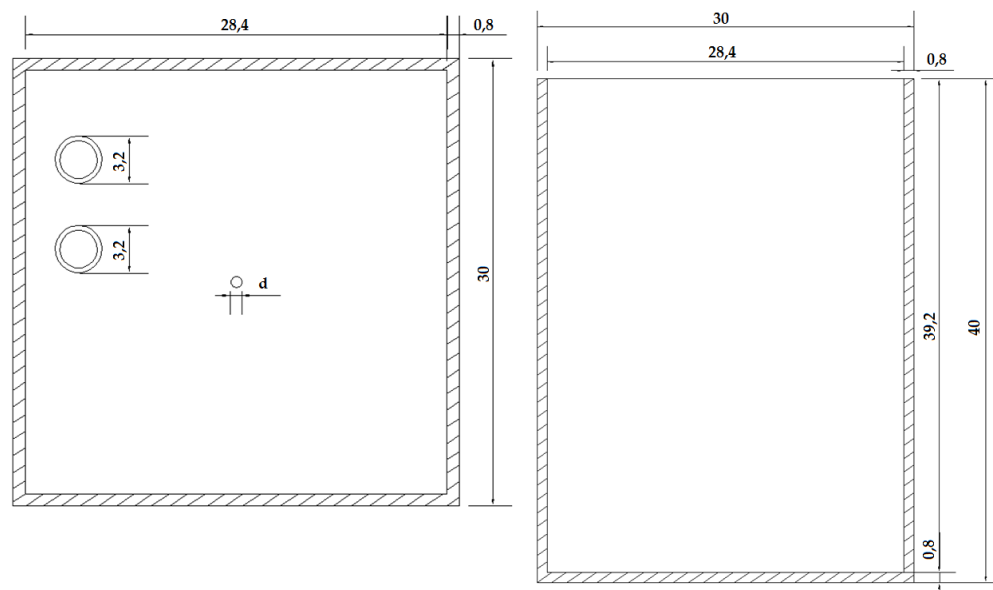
Pianta (a sinistra) e prospetto (a destra) del serbatoio
